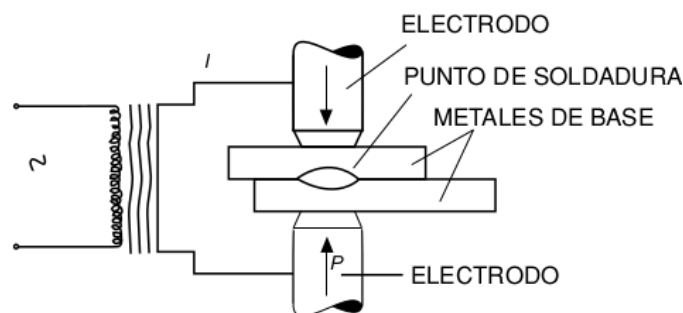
Detalle del proceso de soldadura por puntos. Fotografía obtenida de la web GasolSRL.com
